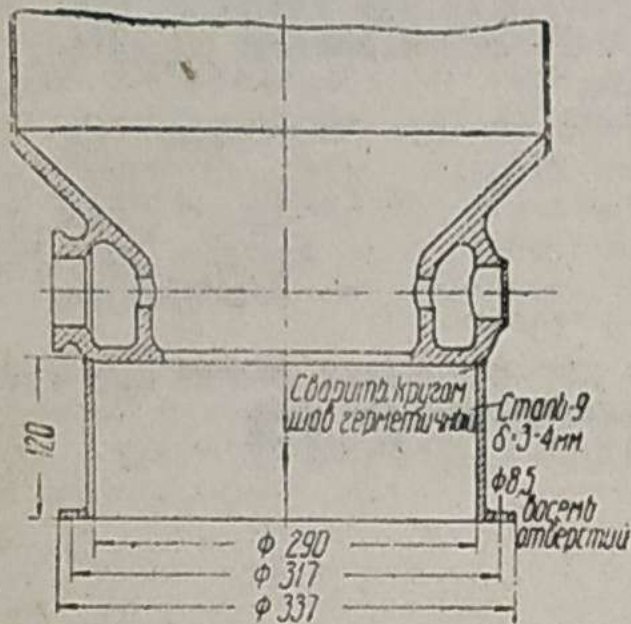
Приварка цилиндра для монтажа горловины ГАЗ-42.
